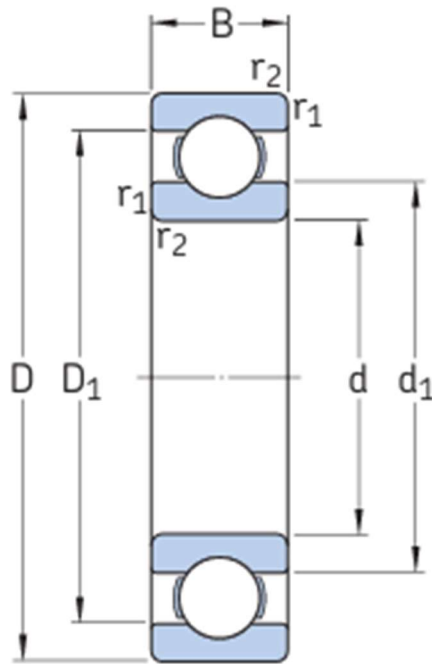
Rodamiento seleccionado. (Fuente: [23])
